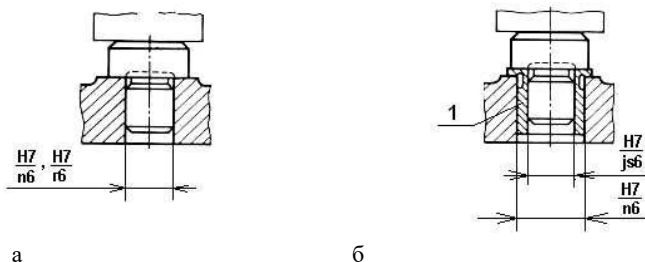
Варианты установки точечных опор в корпусе приспособления:
